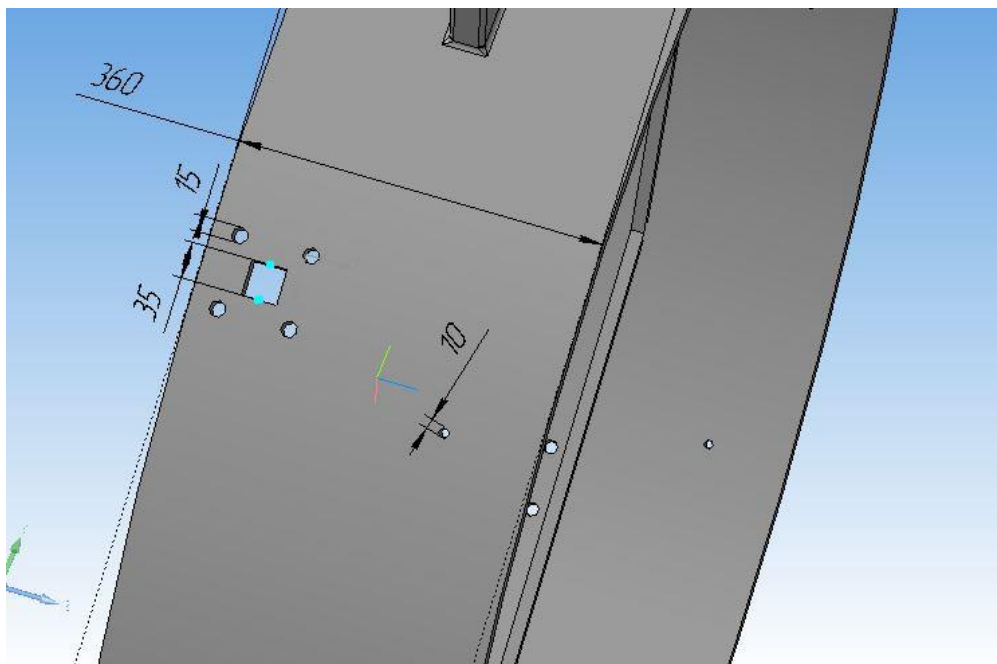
Отверстия крепления Актуатора и направляющего кольца сварочного комплекса «Протеус»
